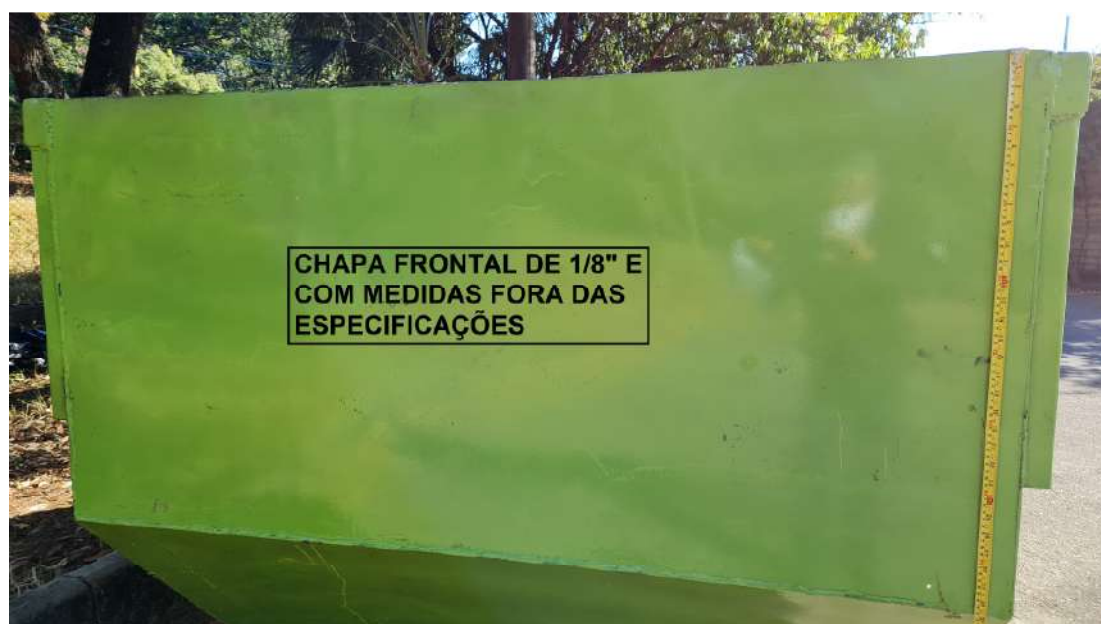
chapa frontal 1/8” e com medidas fora das especificações
